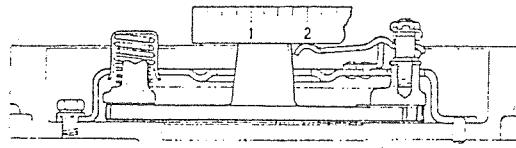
Justering av koppling med användande av jiggplatta, verktyg Saab 92-29.
